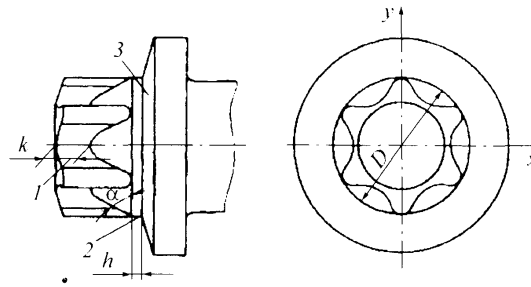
Элементы профилей зацепления головки крепежного стержневого изделия с наружным профилем типа "TORX": 1 – шестирадиусный контур зацепления; 2 – цилиндрический участок; 3 – фланец; h – высота цилиндрического участка; k – высота наружного шестирадиусного контура зацепления; D – диаметр описанной окружности профиля элемента зацепления
